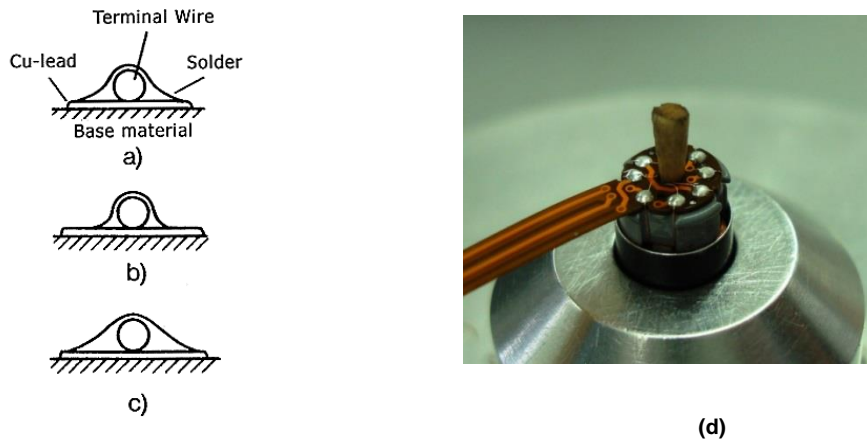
schéma représentant la qualité d'une soudure. (a) optimal. (b) minimum. (c) excessive. (d) Photo d'une soudure bien réalisé sur un moteur pas à pas DM1220 de FAULHABER.
